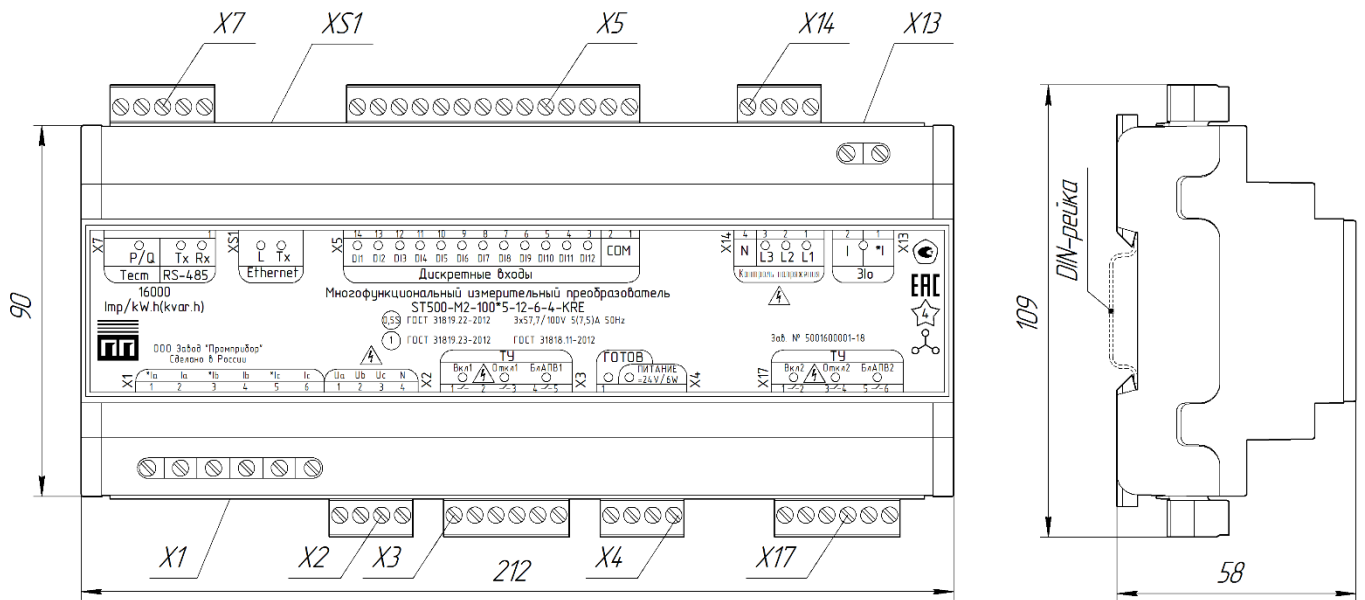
Внешний вид и габаритные размеры МИП
